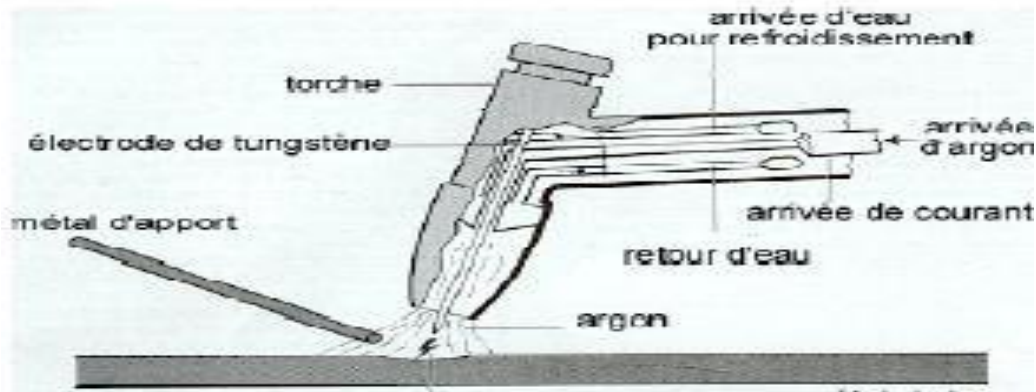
Principe procédé de soudage TIG[12]
